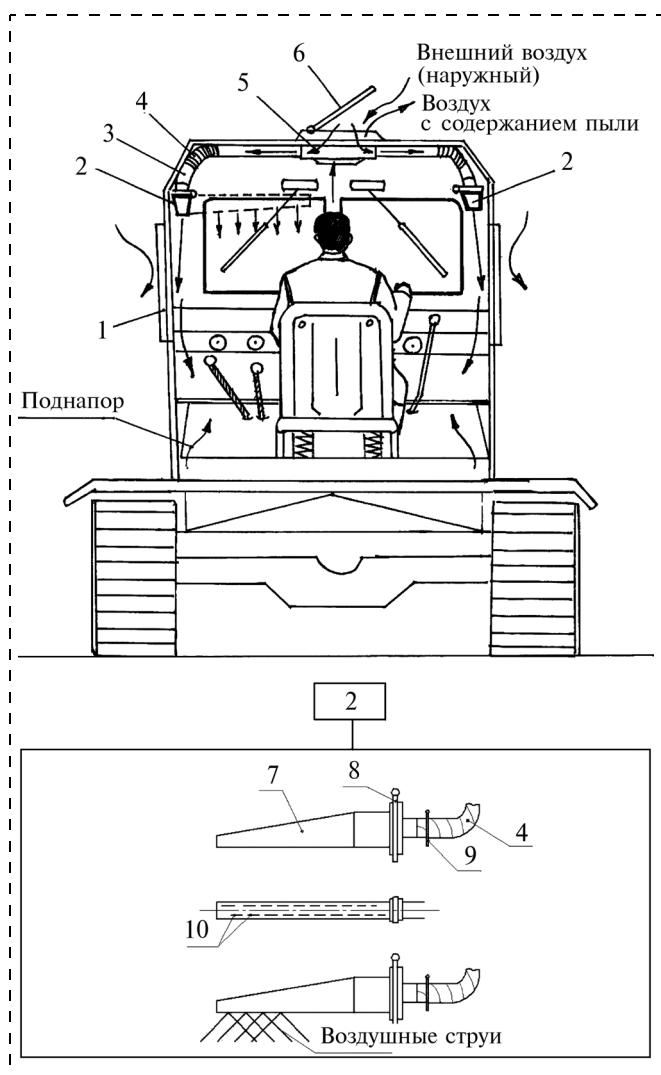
Принципиальная схема устройства (воздушная завеса): 1 — окно; 2 — воздухораспределители; 3, 4 — соединительные патрубки; 5 — вентилятор с фильтром; 6 — люк; 7 — корпус воздухораспределителя; 8 — механизм поворота воздухораспределителя; 9 — соединительный хомут; 10 — отверстия (пазы) для воздуха
